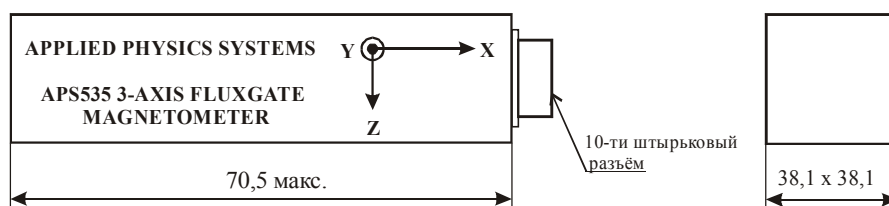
Внешний вид и габаритные размеры датчика типа APS-535
